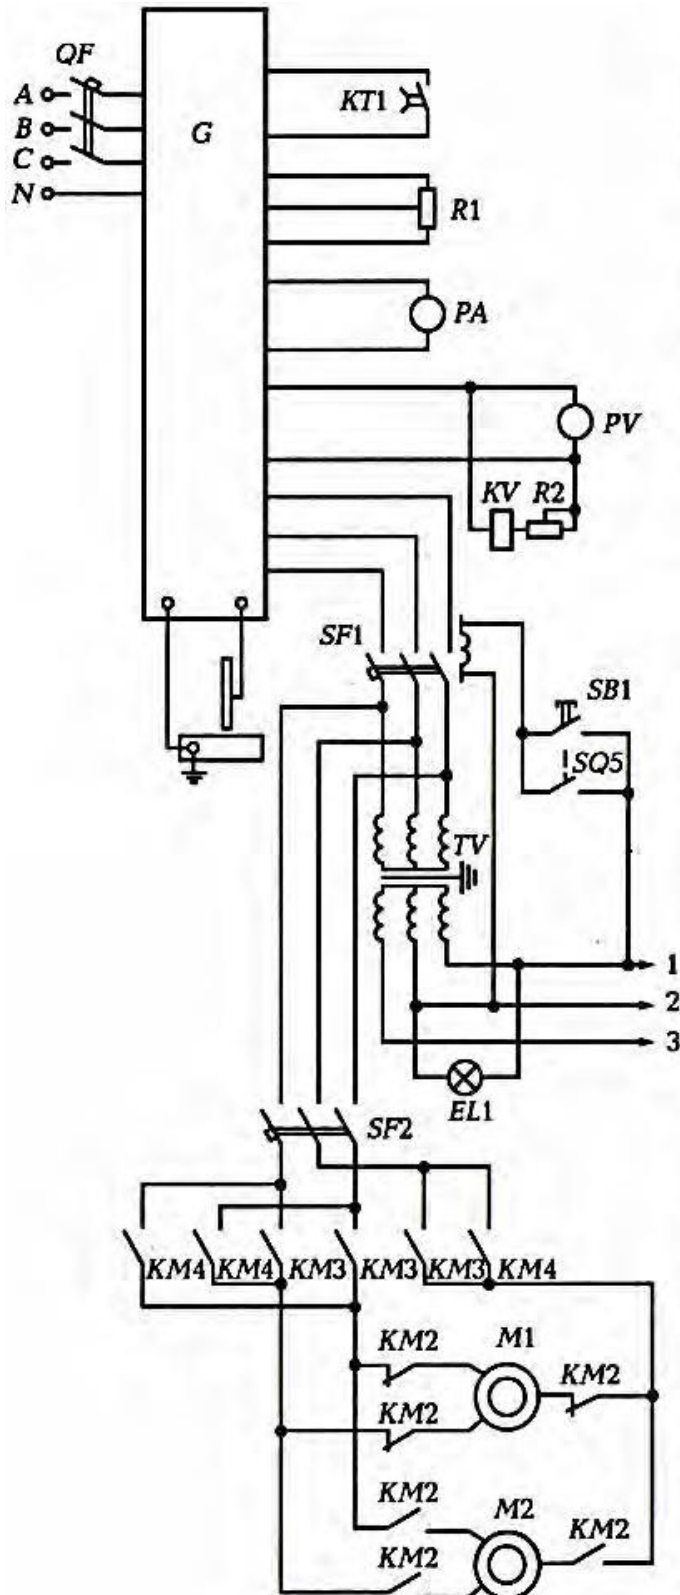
Панель управления сварочного автомата А-1416
